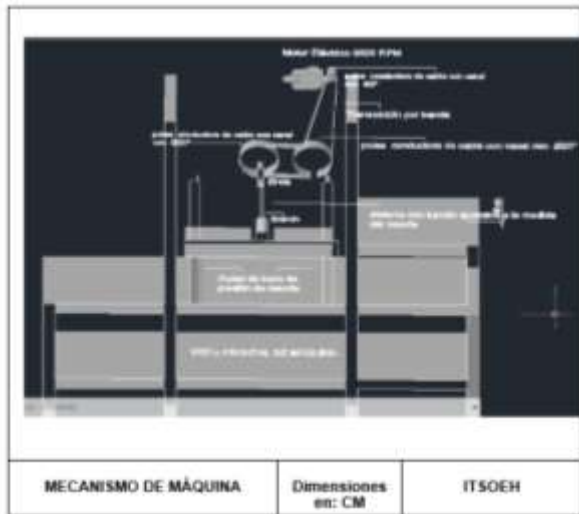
Diseño de la máquina junto con los componentes mecánicos.
